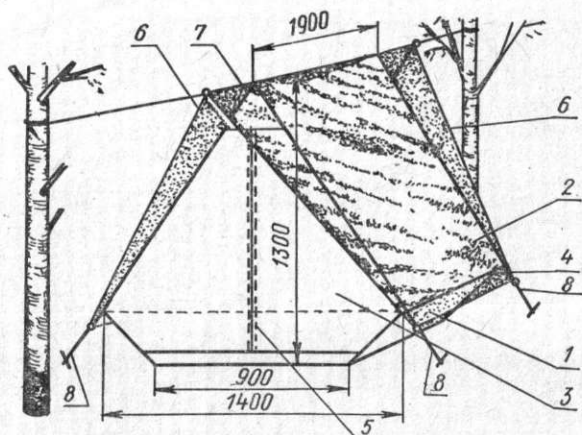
Общий вид палатки конструкции Ю. Рапопорта.
